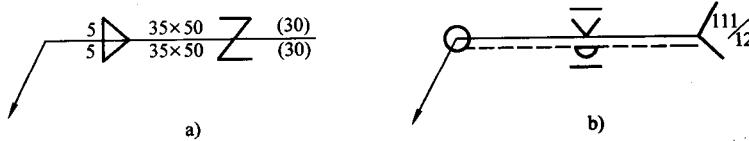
12 焊缝符号和焊接方法代号标注举例
